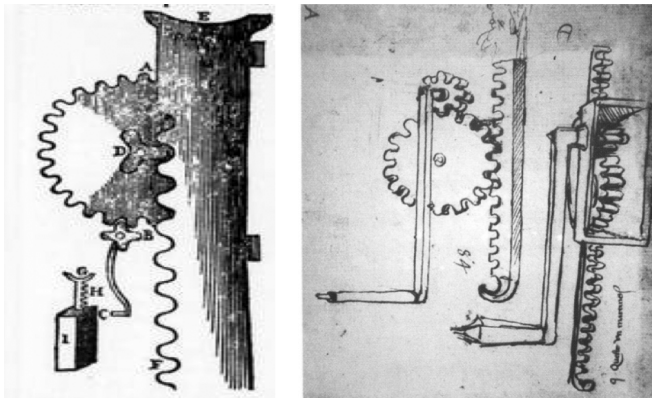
Слева чертеж механизма для преобразования вращательного движения в поступательное, сделанный Галилео Галилеем¹⁹, а справа – Леонардо да Винчи²⁰. Эта машина состоит из кривошипа, понижающей передачи и стержня с зубцами, который движется вверх и вниз.
